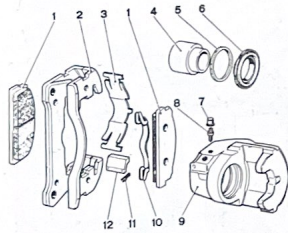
Despiece del mecanismo de frenos delanteros.
